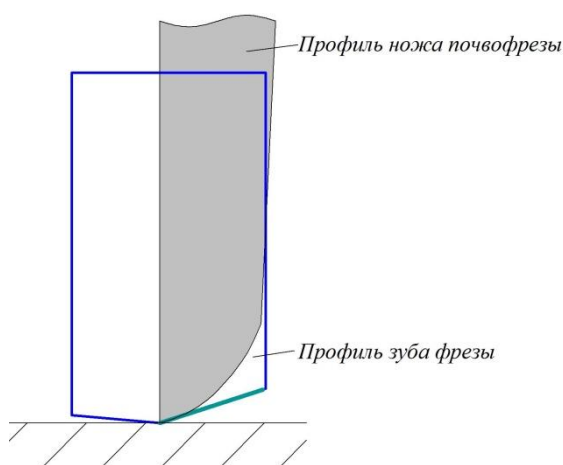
Профили зуба фрезы и ножа почвофрезы
